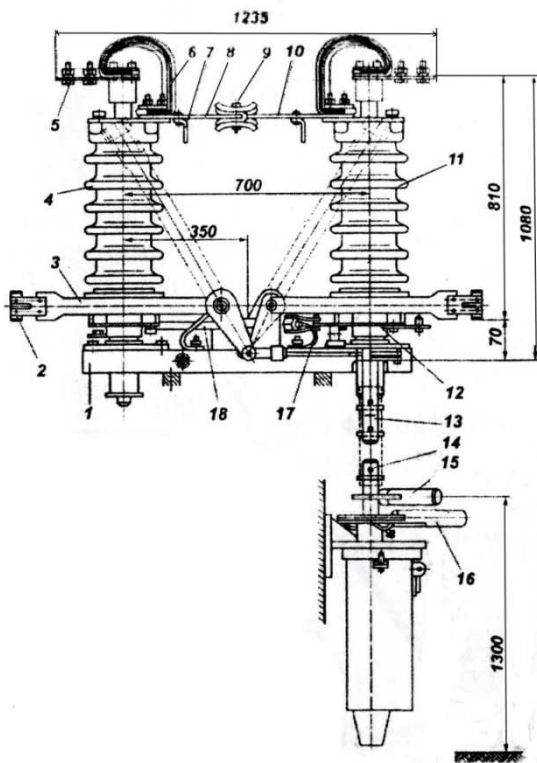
Разъединитель горизонтально-поворотного типа на напряжение 35 кВ для наружной установки:
